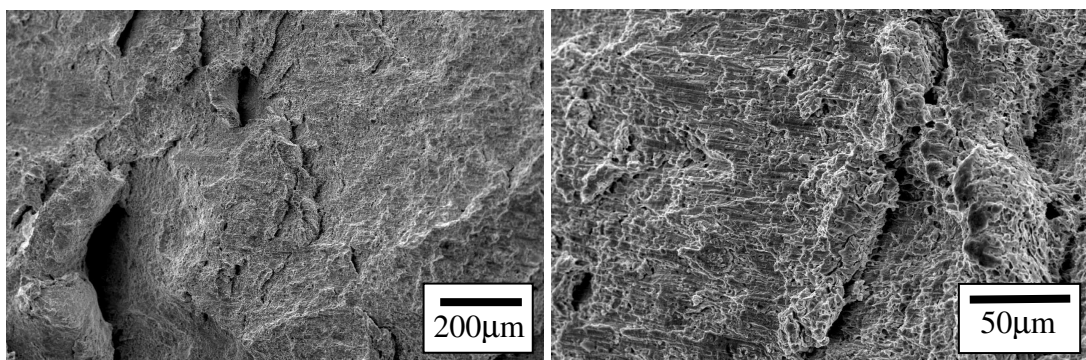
Superfície da fratura ocorrida durante processamento por EACI.
